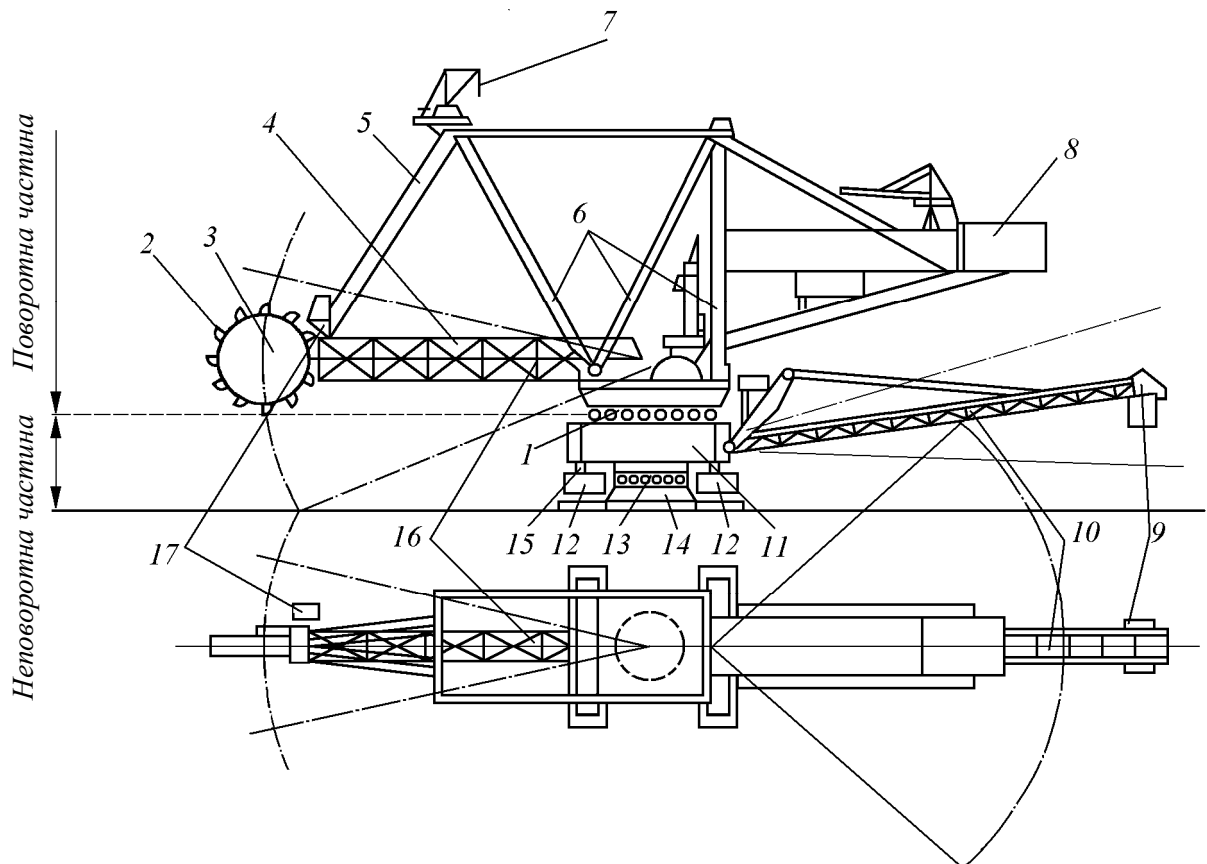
Компоновальна схема роторного екскаватора
